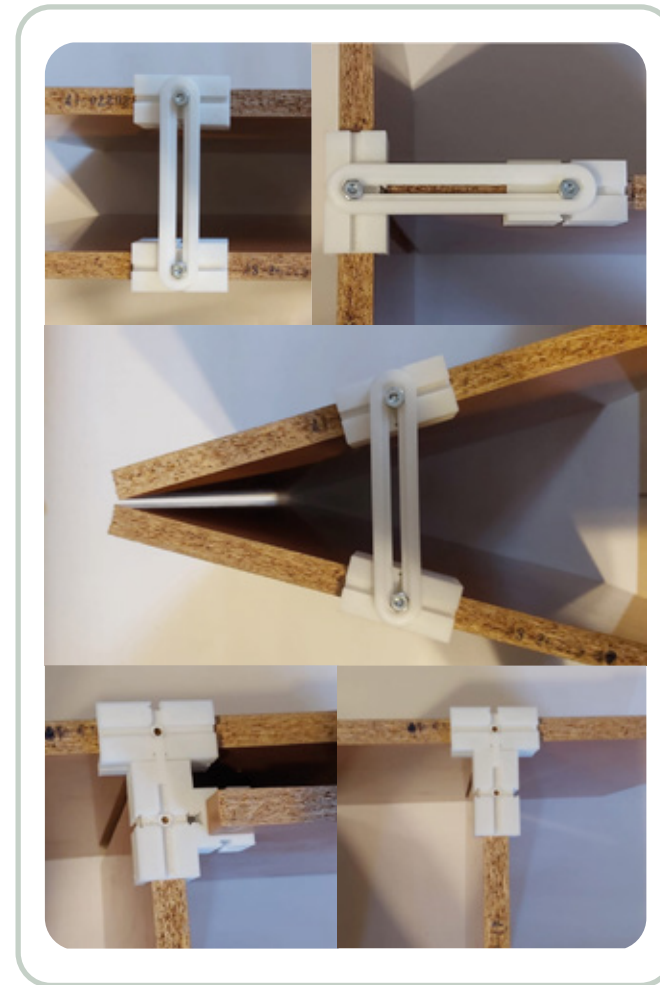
Pruebas de uso set de piezas (propuesta A).
